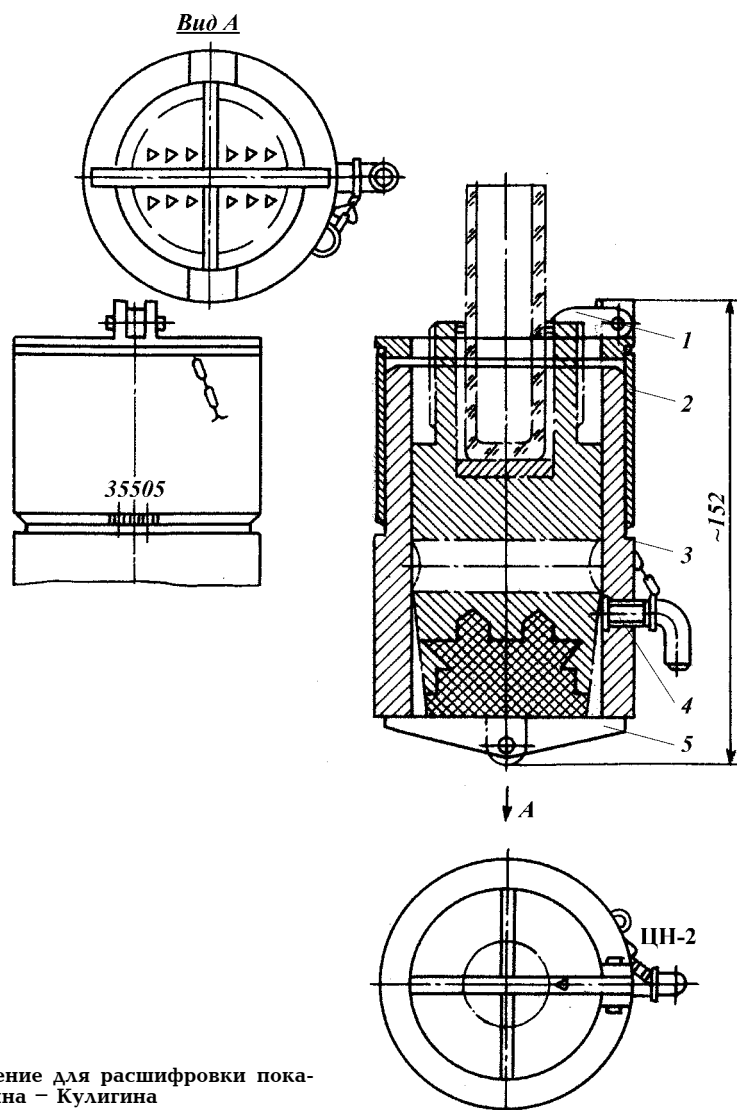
Приспособление для расшифровки показаний аппарата Шаньгина – Кулигина
